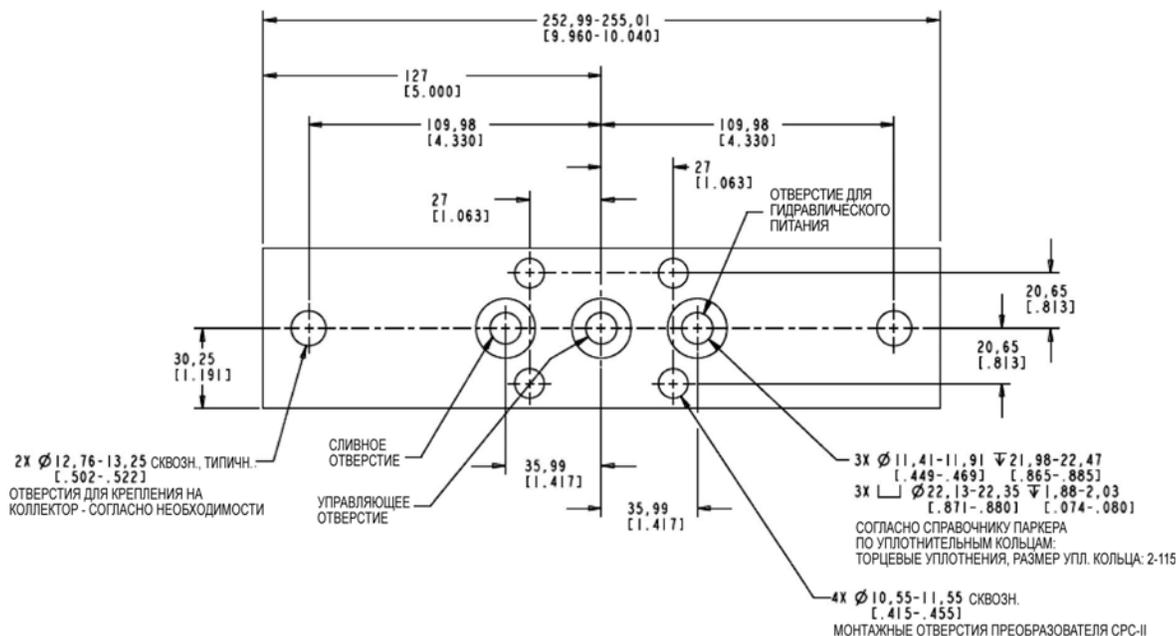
Образец размеров коллектора преобразователя CPC-II
